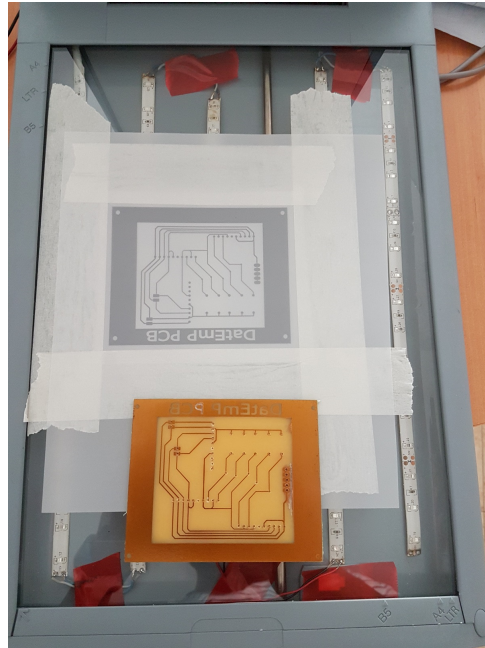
Proceso de insolación del fotolito sobre placa fotosensible para la fabricación de la PCB.
